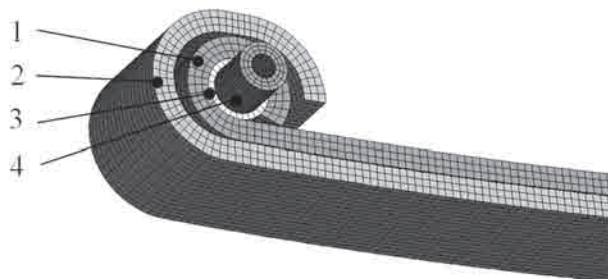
Конечно-элементная модель для моделирования испытаний рессоры с двумя витыми ушками:
